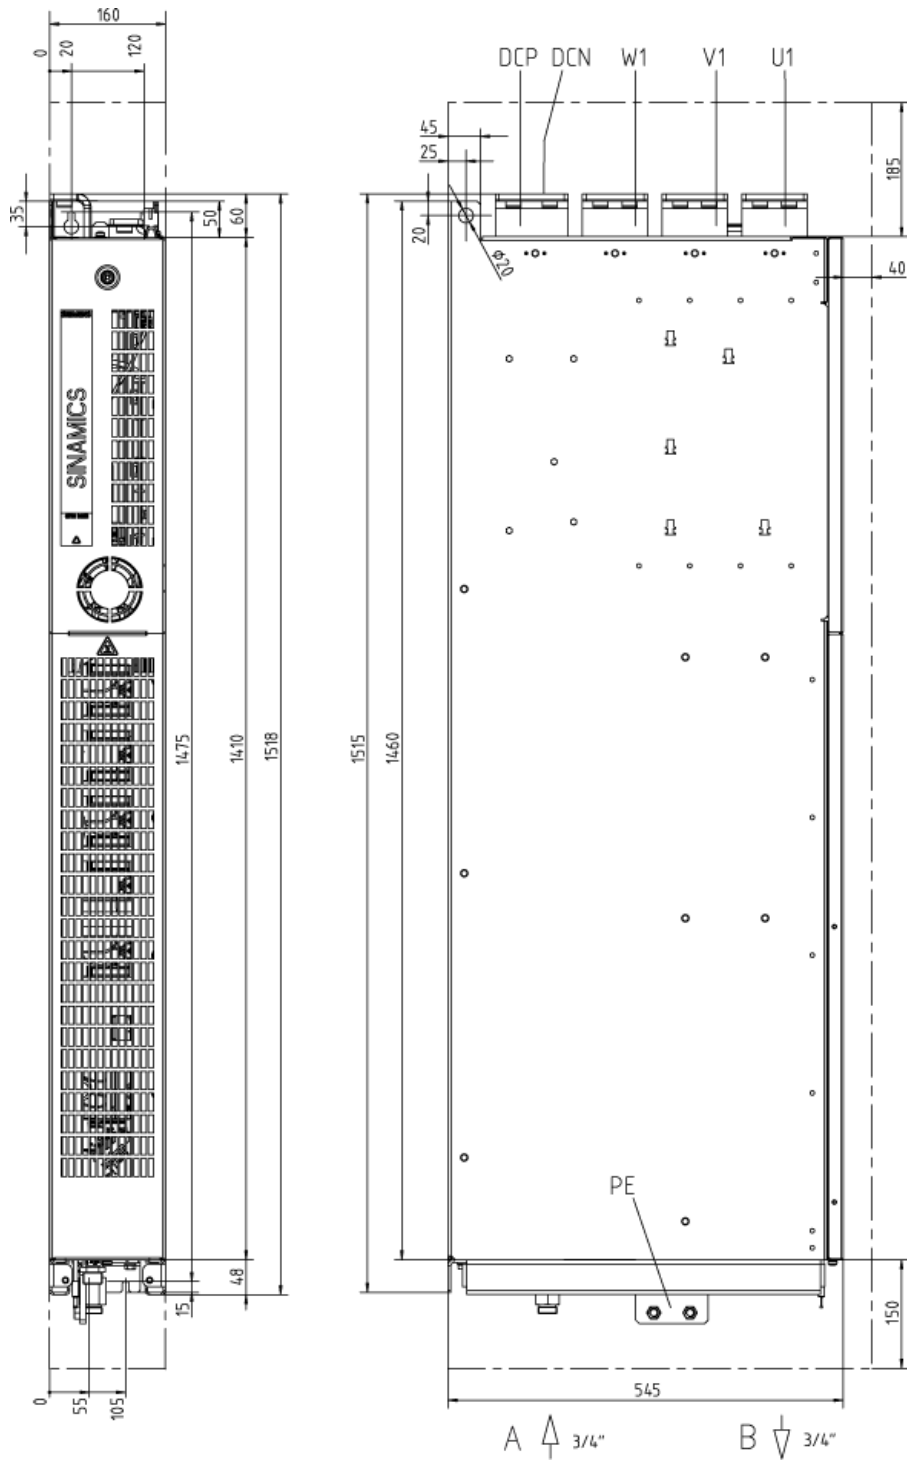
Габаритный чертеж, модуль питания Basic, типоразмер GBL. Вид спереди, вид сбоку
